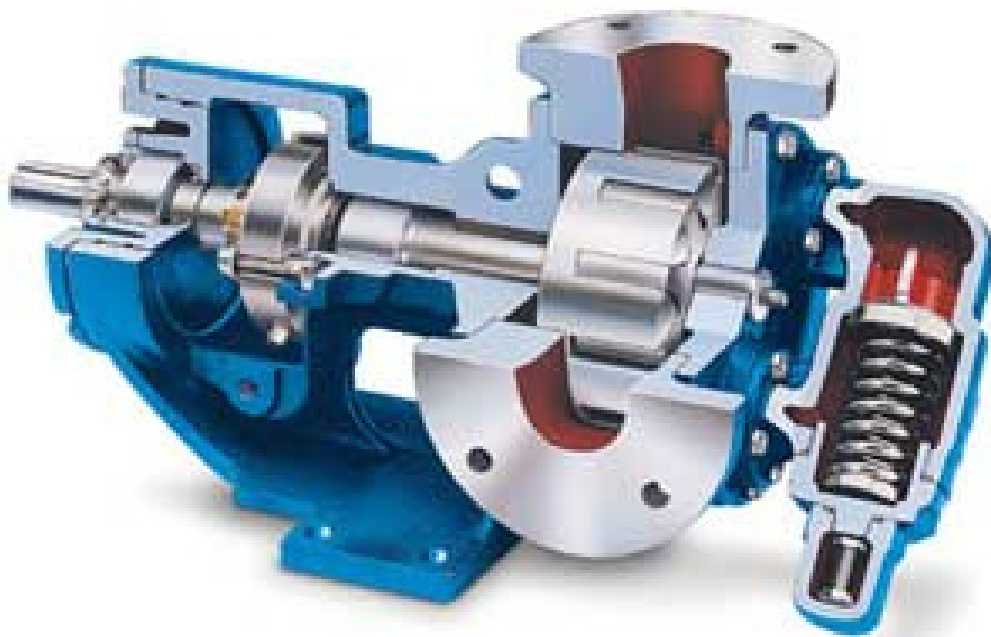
Bomba de engranajes externos      Fig. N° 6 Bomba de engranajes internos
